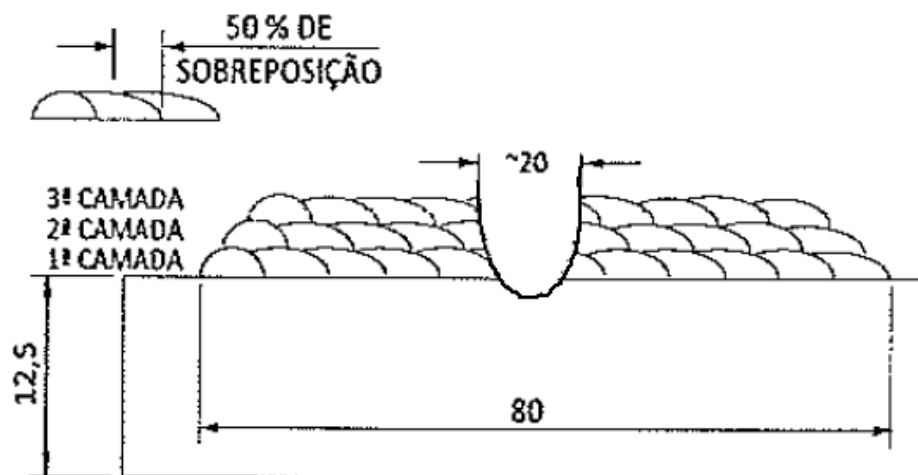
Esquema da Soldagem com Eletrodo Revestido
